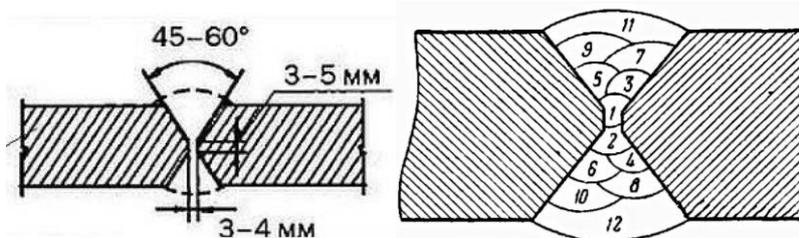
Схемы выполнения валиков в процессе сварки 110 швов, существующая технология:
